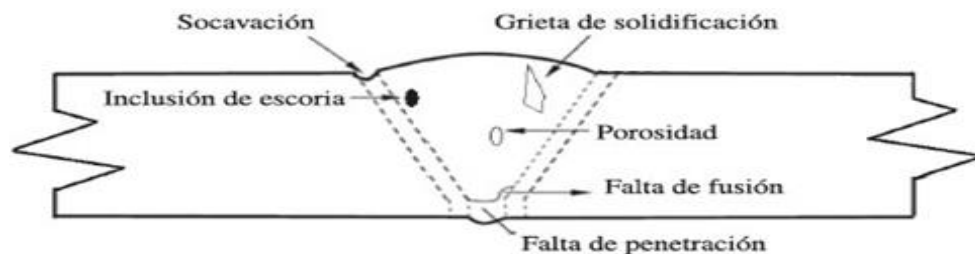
Principales defectos presentes en la soldadura. [40]
